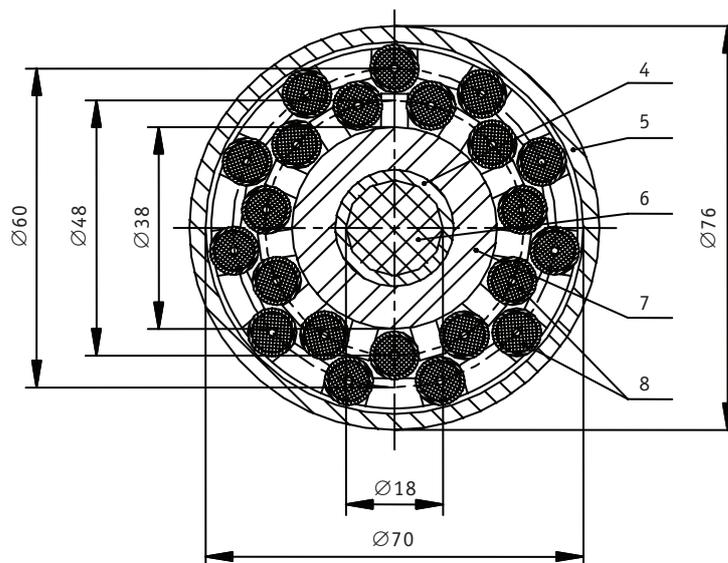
Поперечный разрез ТК реактора ИВГ1.2М в районе активной зоны: 4 – труба для установки поглотителя нейтронов; 5 – корпус ТК; 6 – поглотитель нейтронов; 7 – бериллиевый вытеснитель; 8 – твэл
